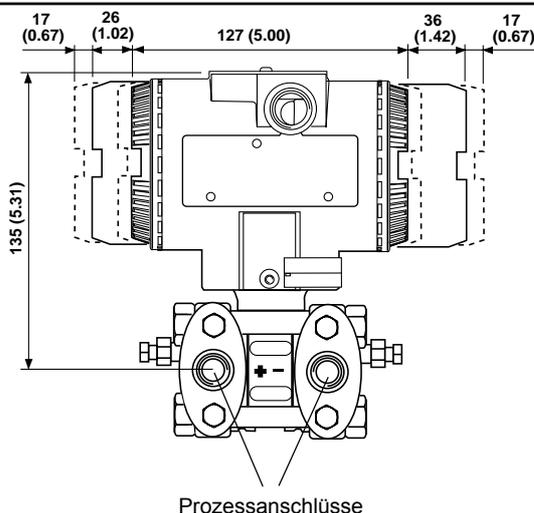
Abmessungen (Differenzdruck-Messumformer) mit Prozessanschlüssen
